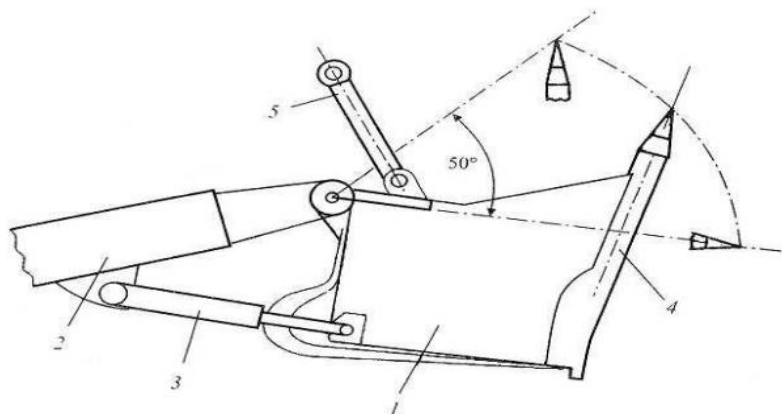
Принципиальная схема поворотного ковша активного действия: 1 – ковш; 2 – рукоять экскаватора; 3 – гидроцилиндр поворота ковша; 4 – пневмоударник; 5 – элемент подвески ковша [73]
